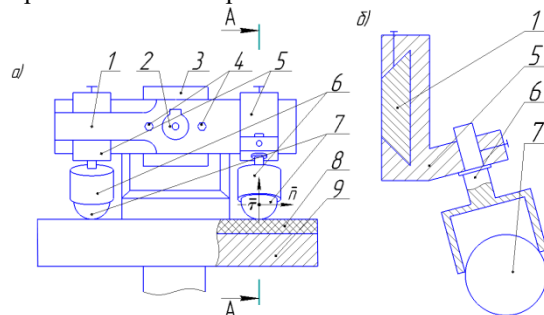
Схема установки приспособления на шлифовально-полировальном станке
